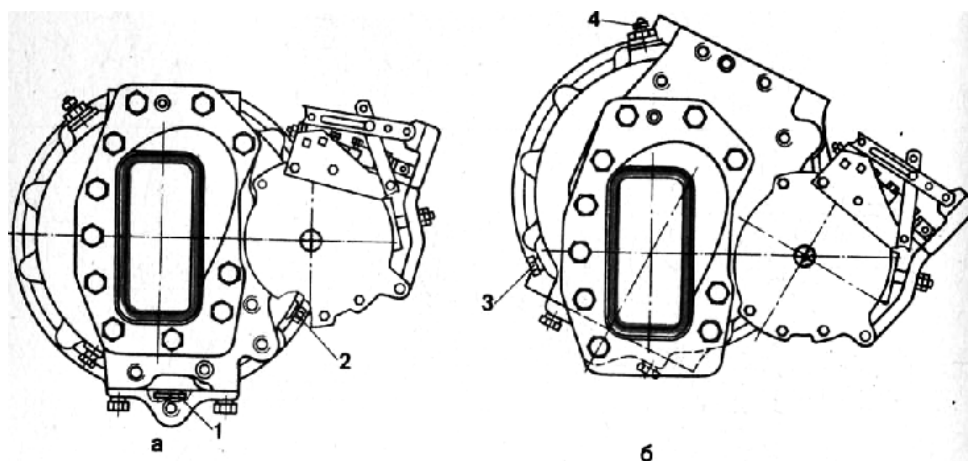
Бортовой редуктор (вид со стороны тормоза):
